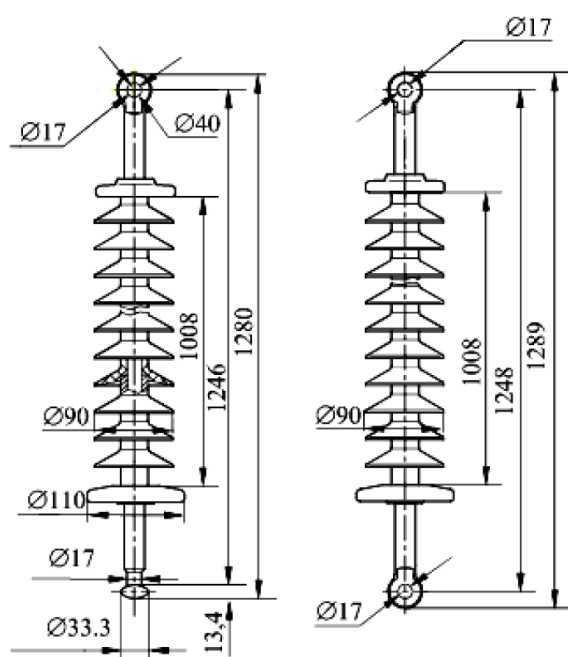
Конструкція композиційного ізолятора ЛК-70/ 110-3
